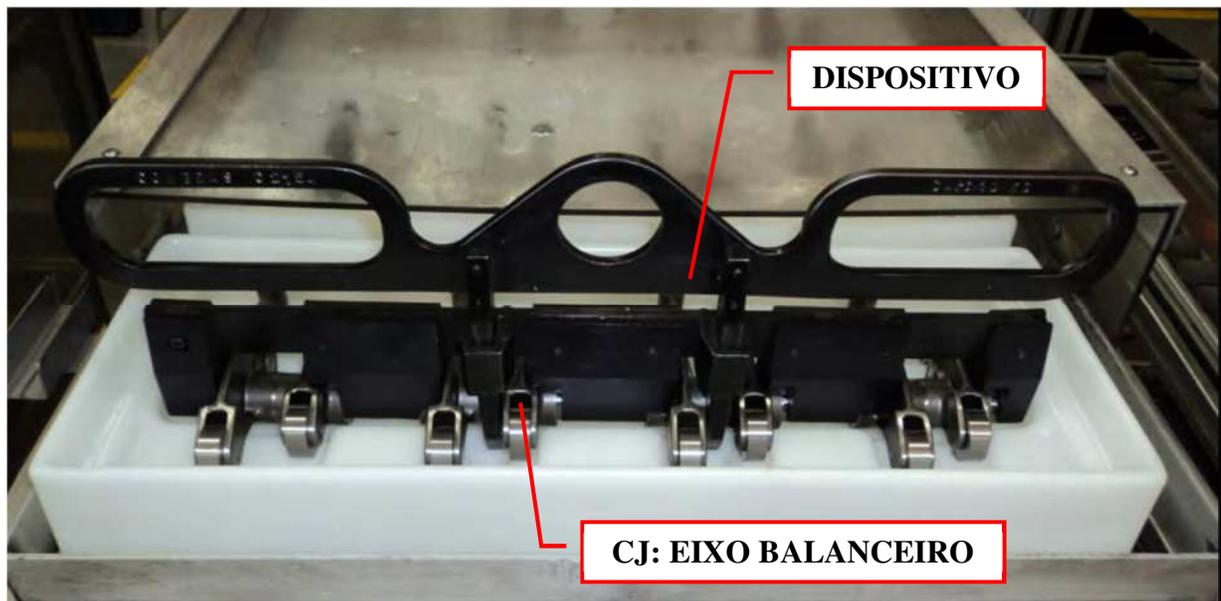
Dispositivo de montagem do conjunto eixo balanceiro do motor NGD3.0E
